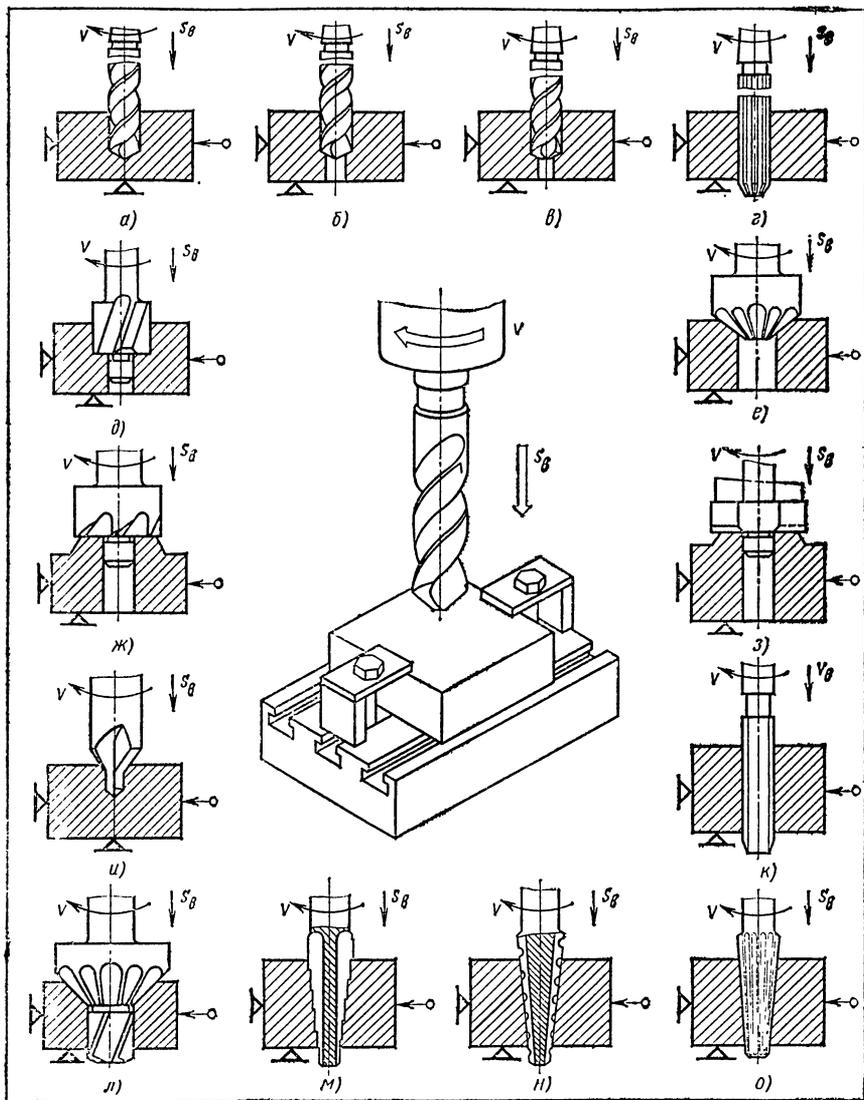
Схемы обработки посерхностей на сверлильных станках
